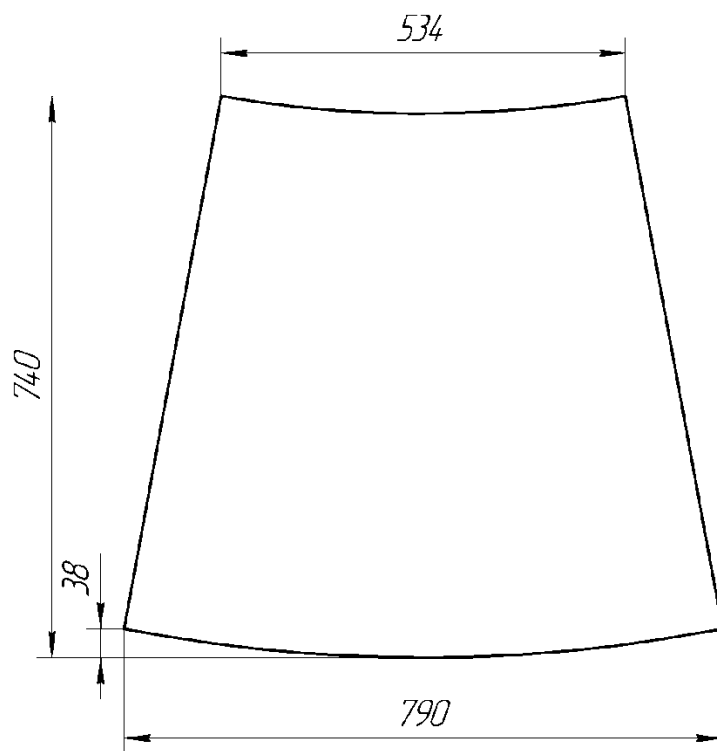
Развертка деталей № 1, 41 обшивки обтекателя
